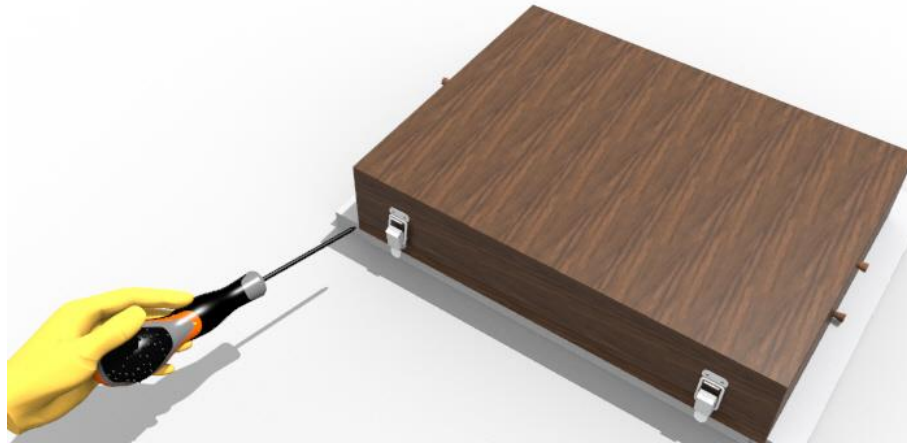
Ensamblaje del asa con el maletín parte 2
